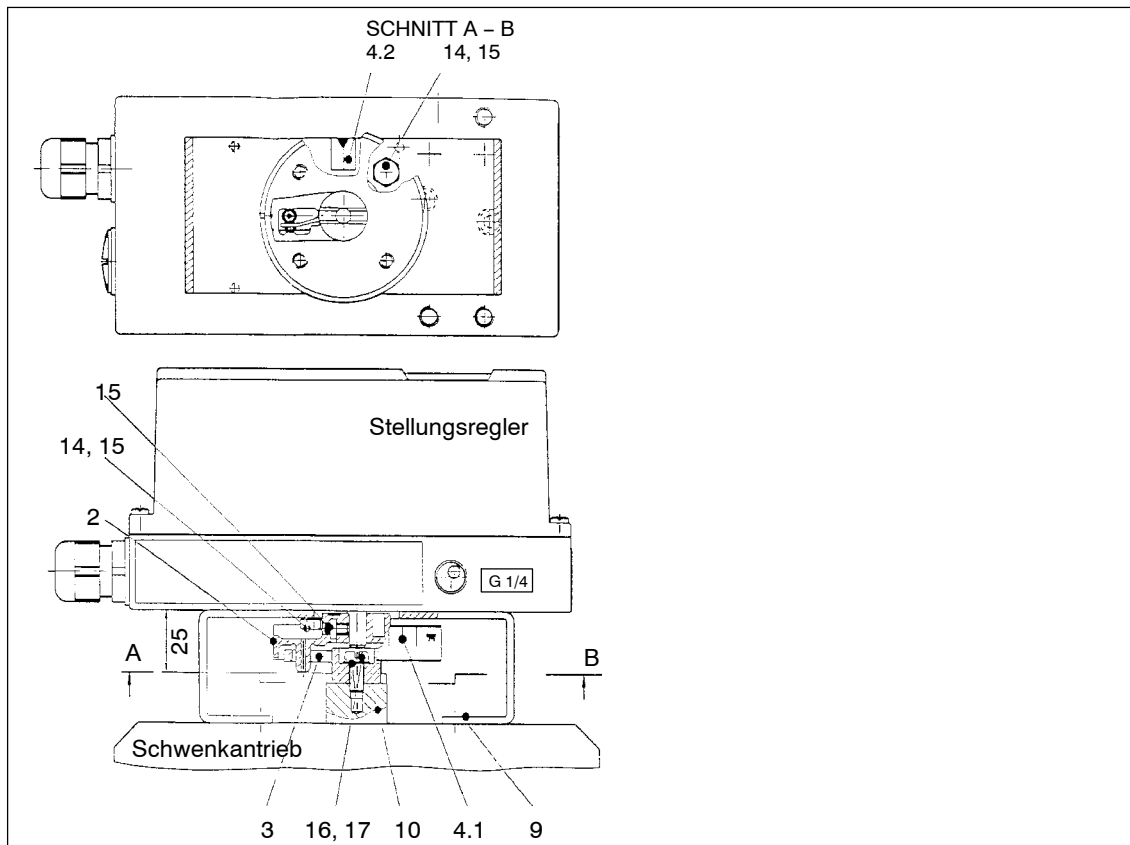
Montageablauf für druckfestes Gehäuse (Schwenkantrieb)
